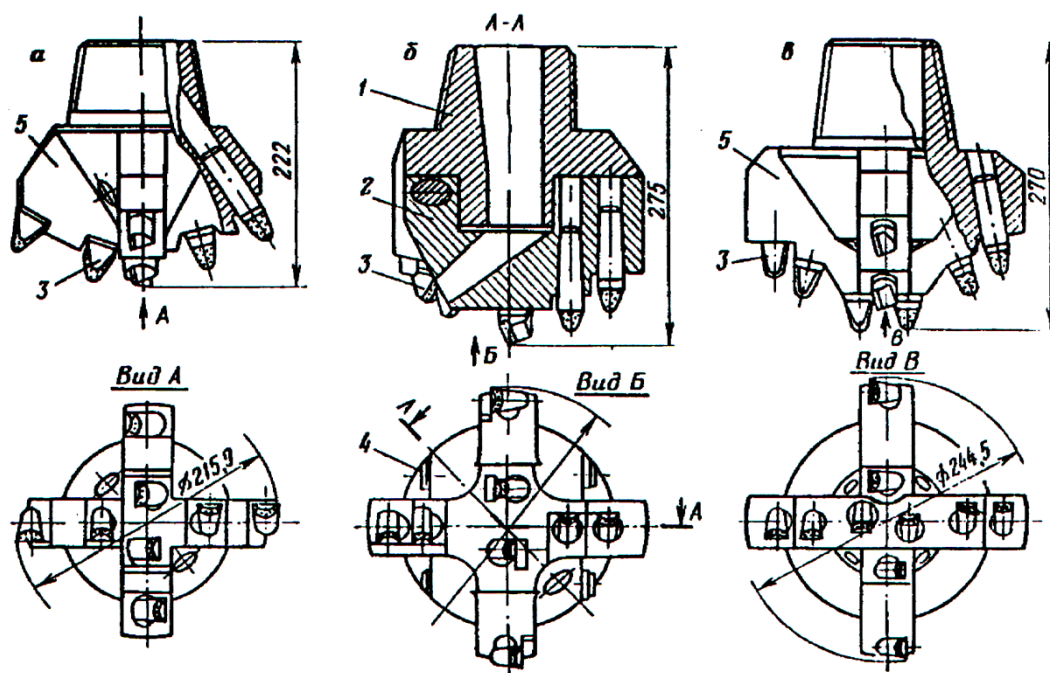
Режущие долота для бурения с продувкой (конструкции Иркутского ГТУ): а – ЗРД215,9; б – 1РД244,5; в – ЗРД244,5; 1 – хвостовик; 2 – съемный корпус; 3 – сменный комбайновый резец; 4 – замковый палец; 5 – корпус долота.
